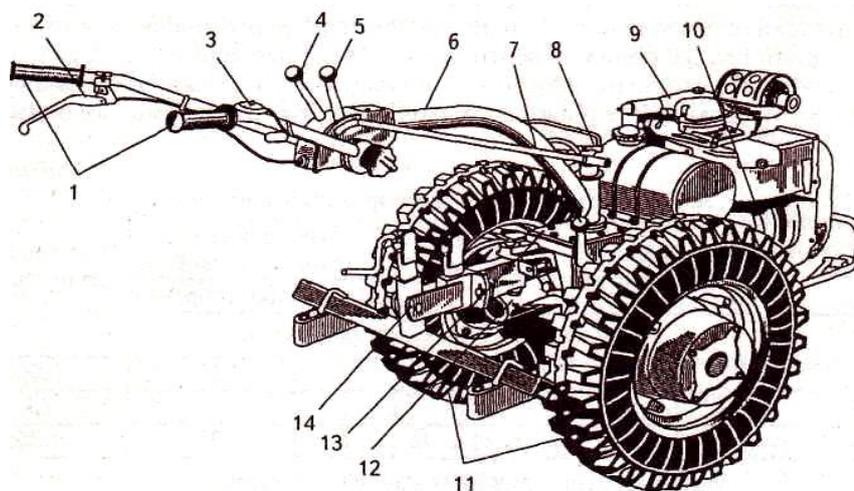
Общий вид мотоблока: 1 – рукоятка управления; 2 – рычаг управления сцеплением; 3 – рычаг газа; 4 – рычаг реверса; 5 – рычаг переключения передач; 6 – рулевая штанга; 7 – рычаг включения вома; 8 – бензобак; 9 – воздушный фильтр; 10 – двигатель; 11 – колеса; 12 – сцепка вома; 13 – стойка; 14 – прицеп
